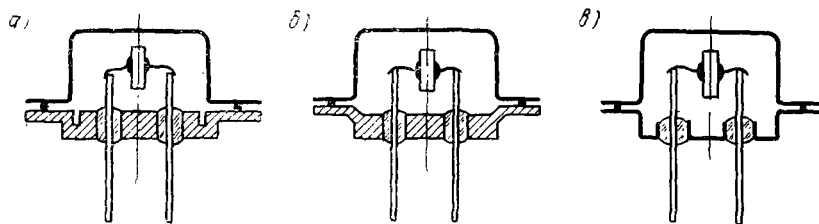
Способы уменьшения деформации центральной части корпуса транзистора при холодной сварке:
